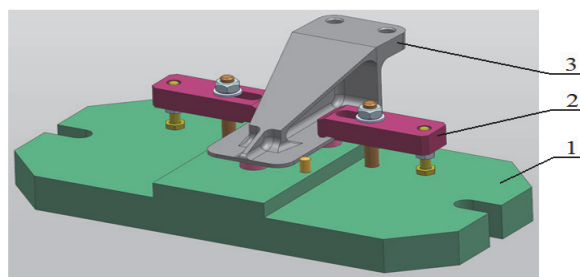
Заготовка детали «кронштейн» в приспособлении
